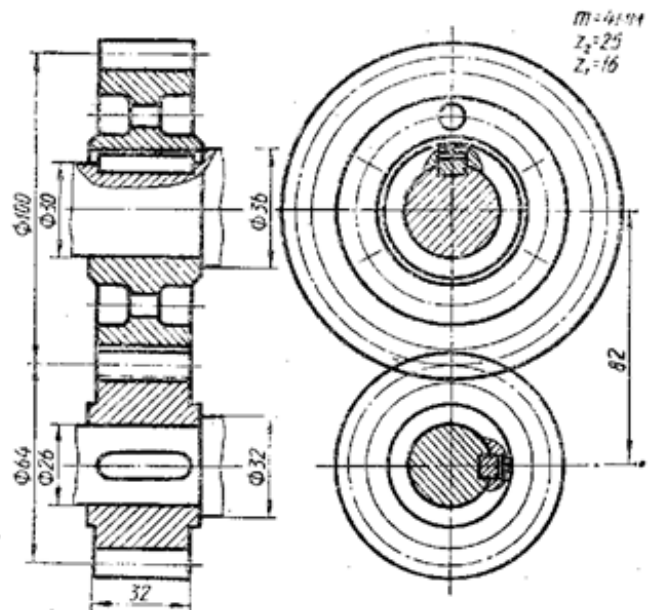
Оформление рабочего чертежа цилиндрического зубчатого колеса
